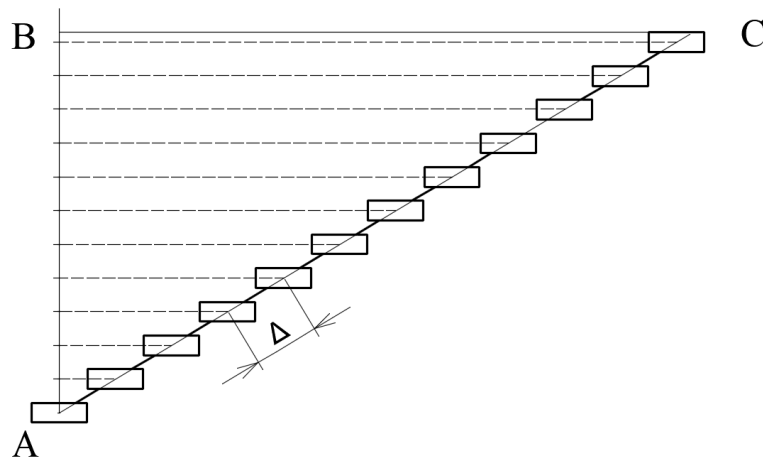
Схема расстановки резцов на шнековой образующей линии фрезы
